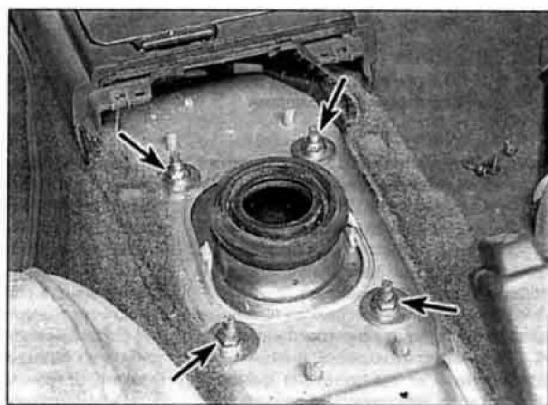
Отверните гайки (показаны стрелками) крепления корпуса рычага
